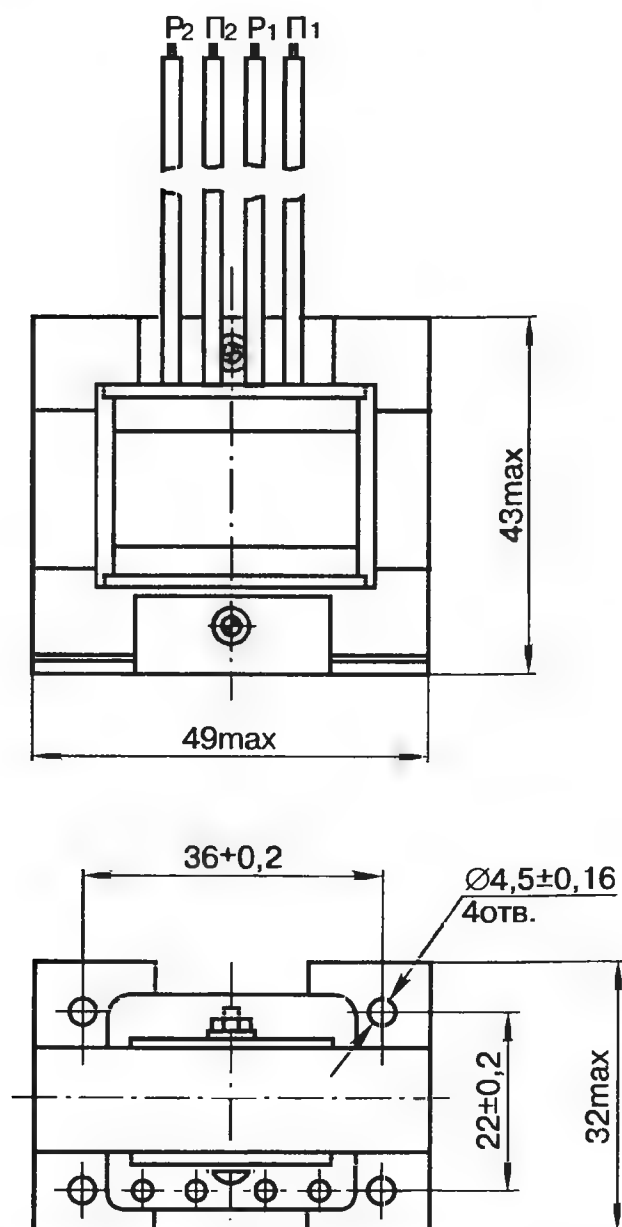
Присоединительные и габаритные размеры трансформатора РТ-3М
